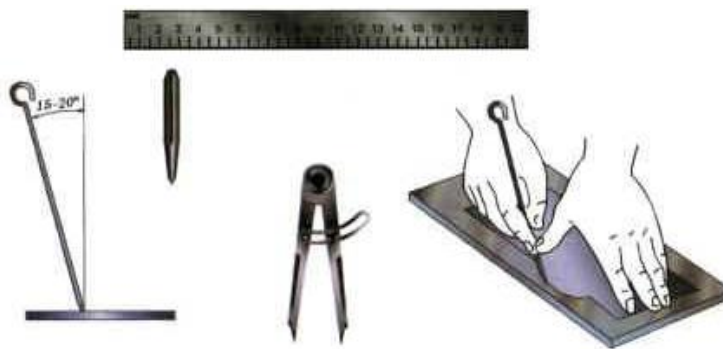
Інструменти для розмітки заготовівлі з металу
